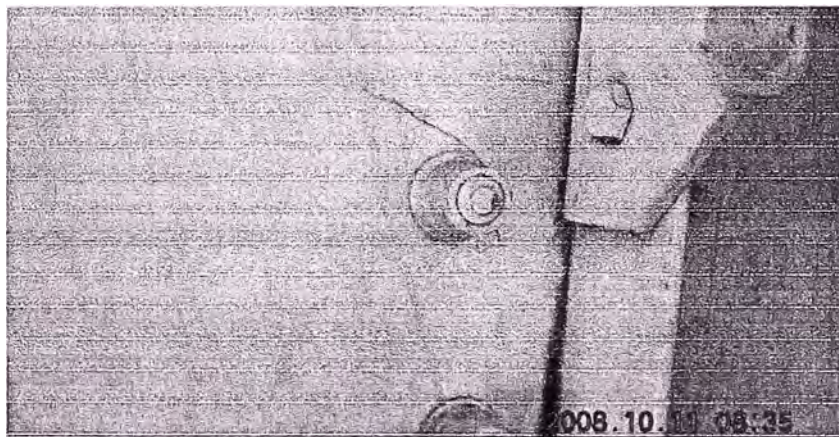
Rotura de Viga Soporte de Excitador (Drive Beam)
